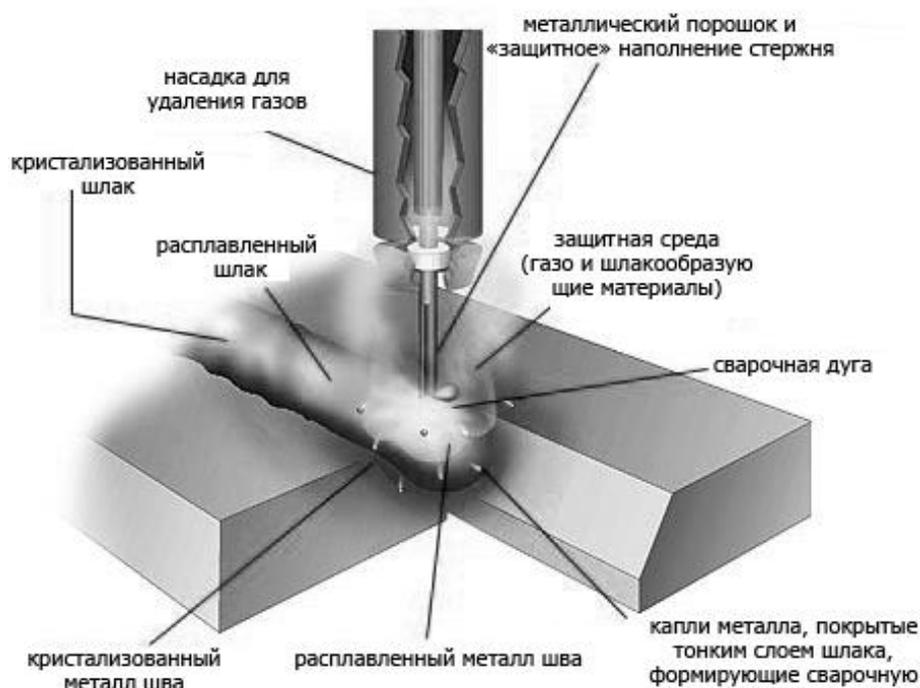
Сварка самозащитной порошковой проволокой
